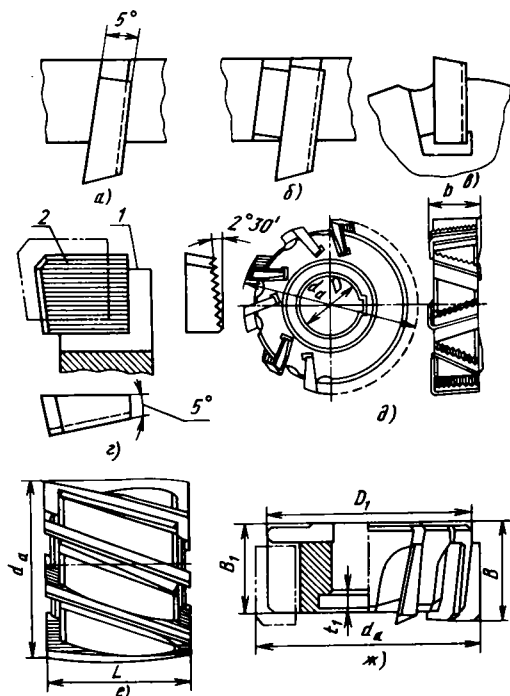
Сборные фрезы из быстрорежущей стали
